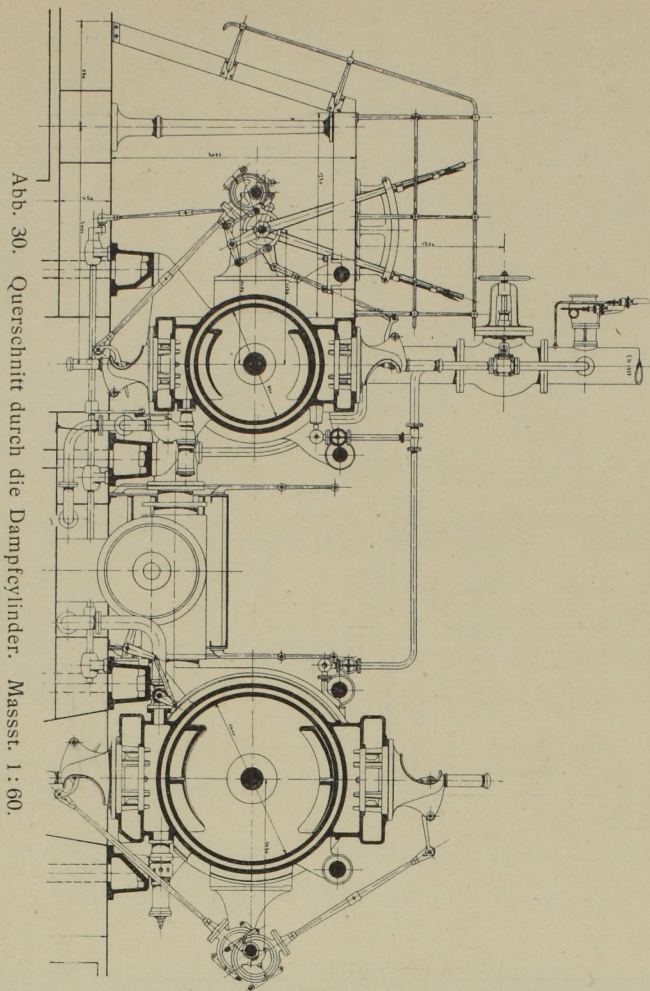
Querschnitt durch die Dampfzylinder. Massst. 1 : 60.
